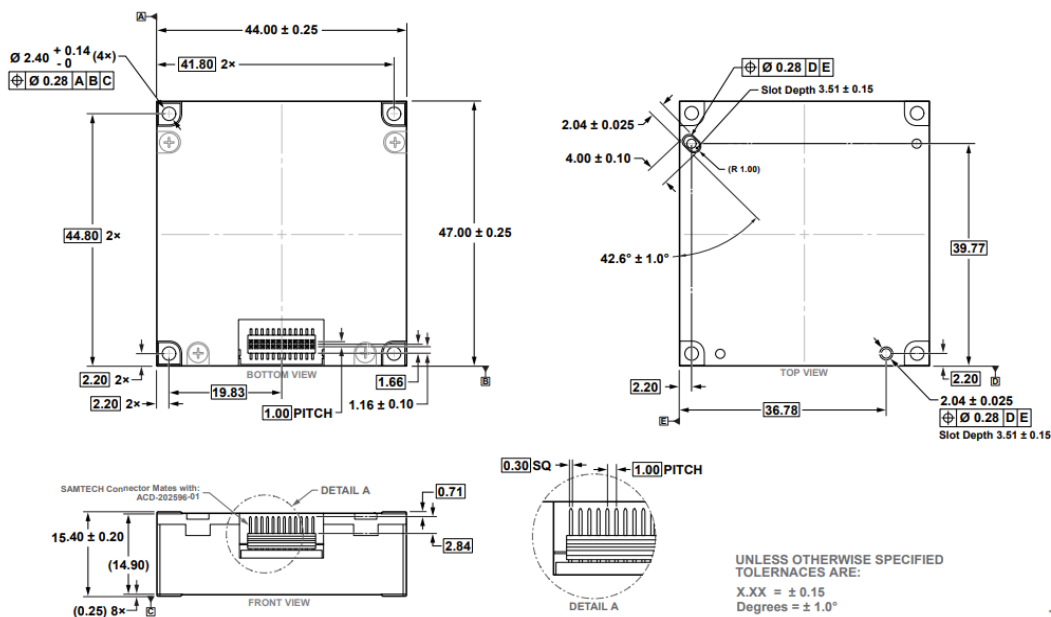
Dimensioni del Package (ML-24-12) in millimetri.
